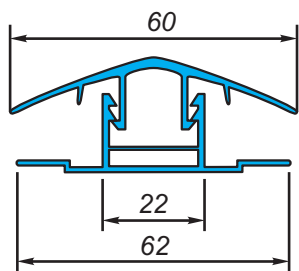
НСР - разъёмный соединительный поликарбонатный профиль.
